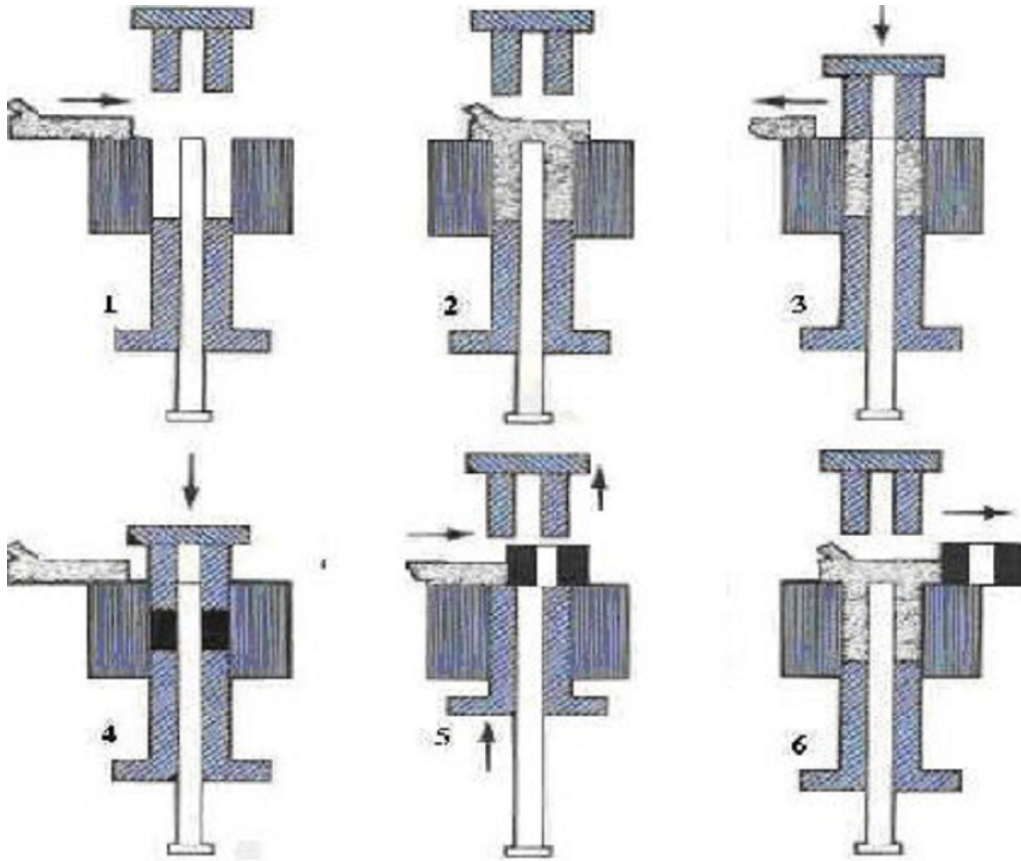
Presleme işleminde kullanılan kalıp ve diğer elemanlar [6].
